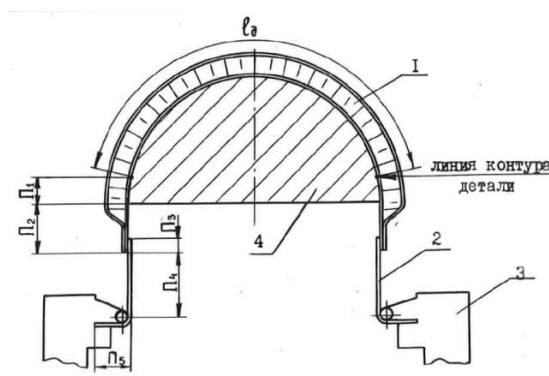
Схема положения заготовки СП с приваренными технологическими пластинами при обтяжке на прессе FEKD 550/1100:
